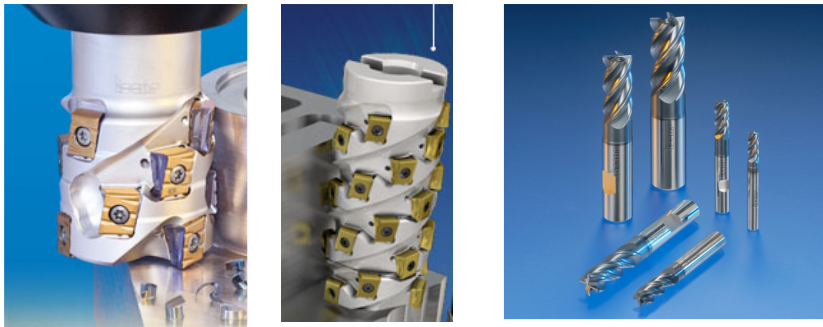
Сучасні конструкції фрез з гвинтовим зубом для периферійного та комбінованого фрезерування
